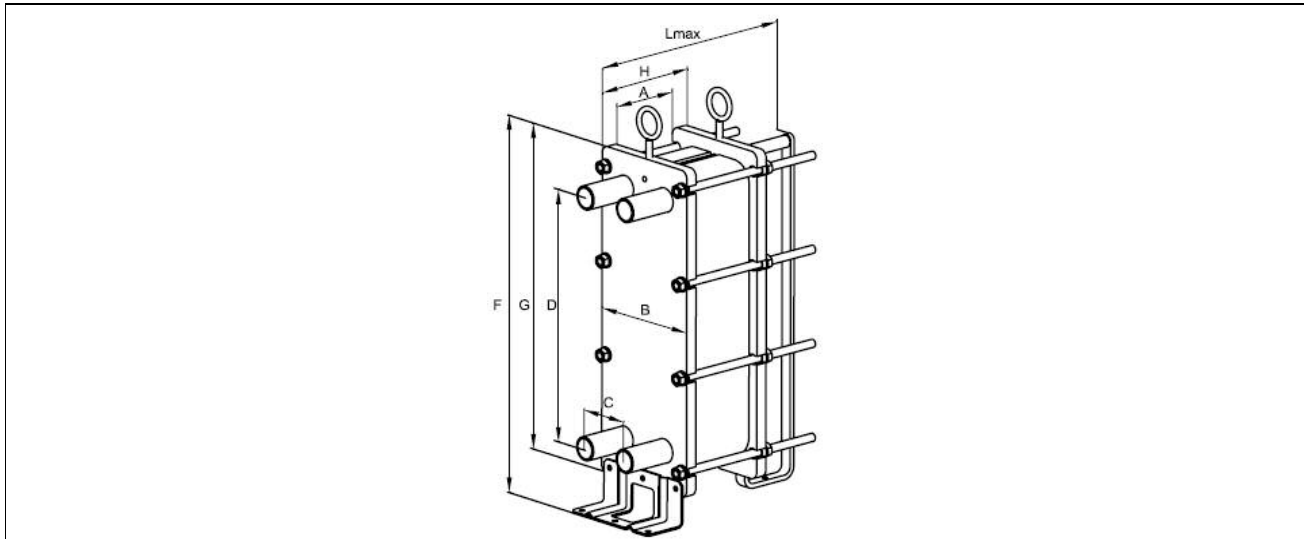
Габаритные размеры теплообменников разборных пластинчатых
